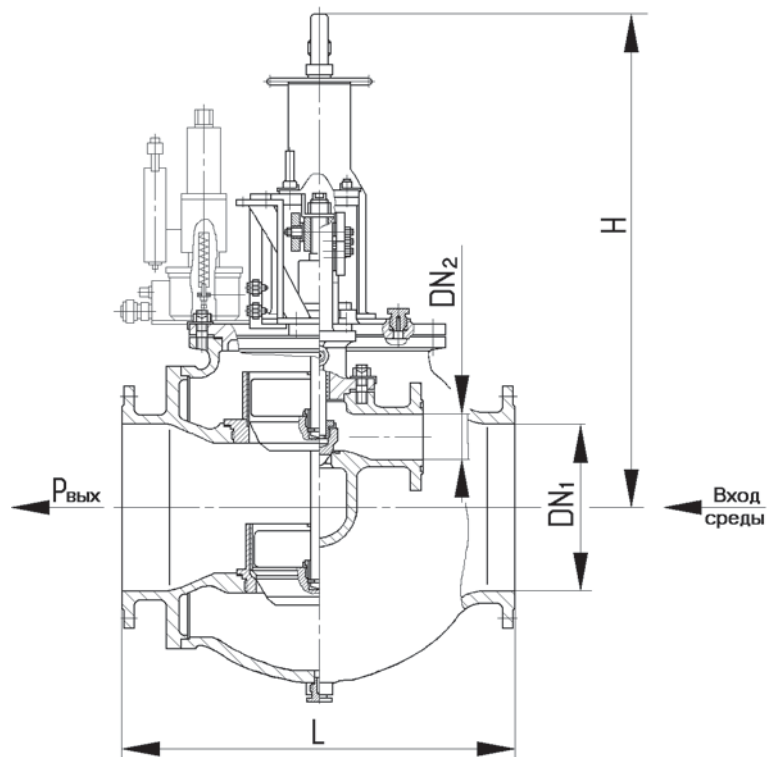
Клапан регулирующий проходной фланцевый сдвоенный с гидроприводом
